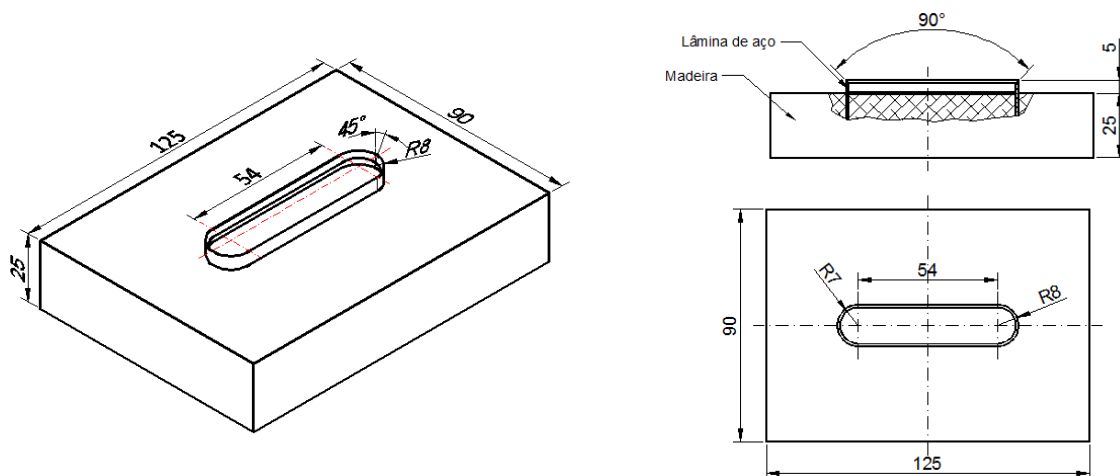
Dispositivo para corte da fita adesiva (dimensões em mm).
